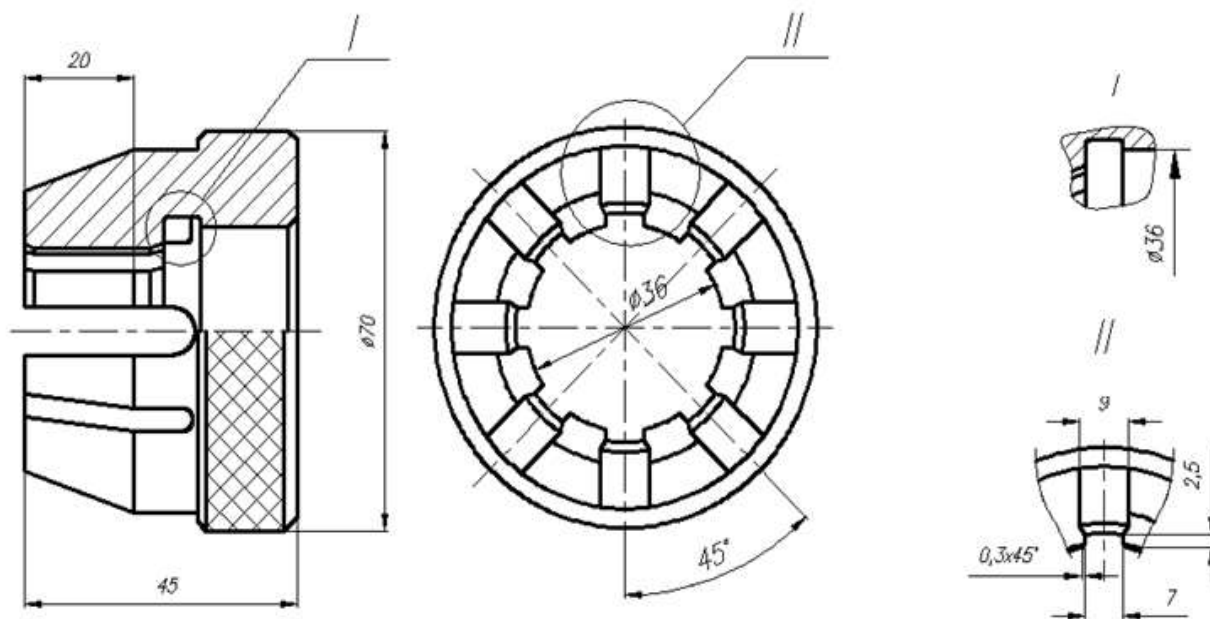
Эскиз калибра –кольца шлицевого прямобочного соединения
